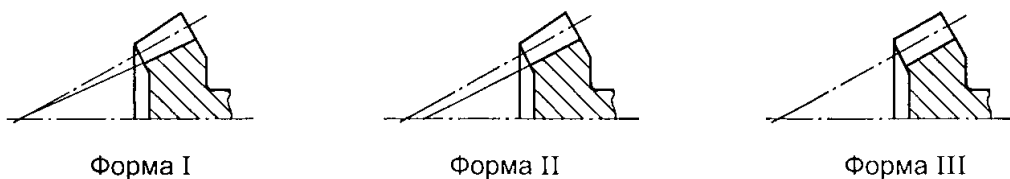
Осевая форма зуба конического зубчатого колеса
